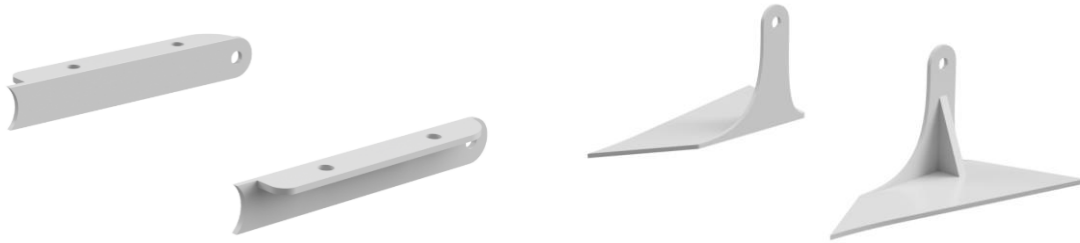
Soportes posteriores (izquierda) e inferiores (derecha) del conjunto motor - depósito
